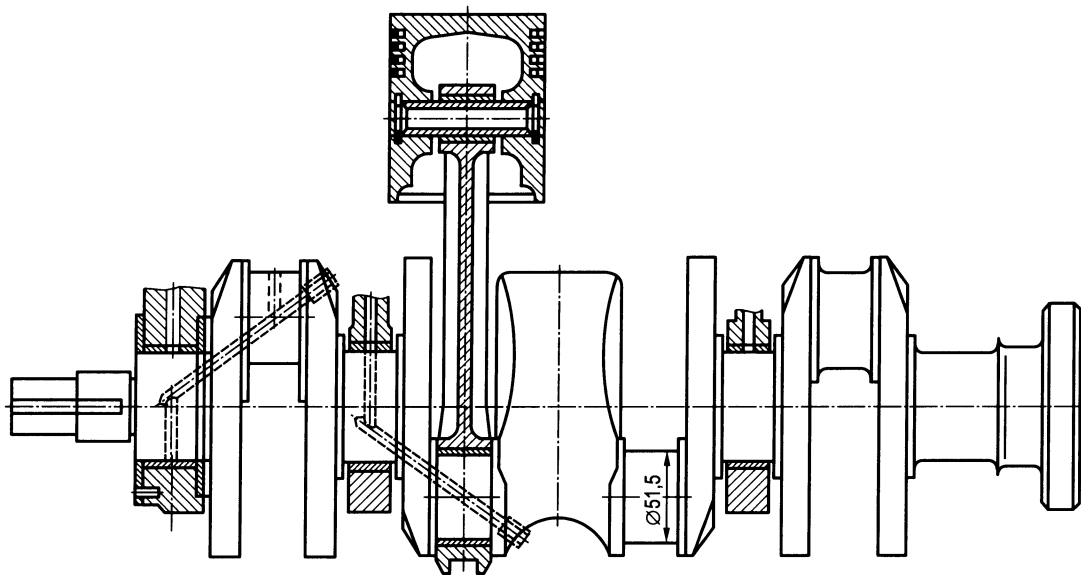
Коленчатый вал двигателя внутреннего сго
